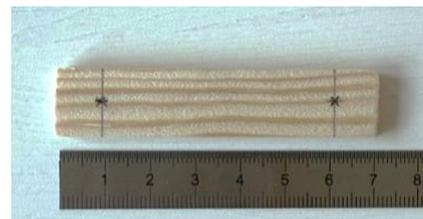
Markierung der Bohrlöcher für die Radbefestigung
